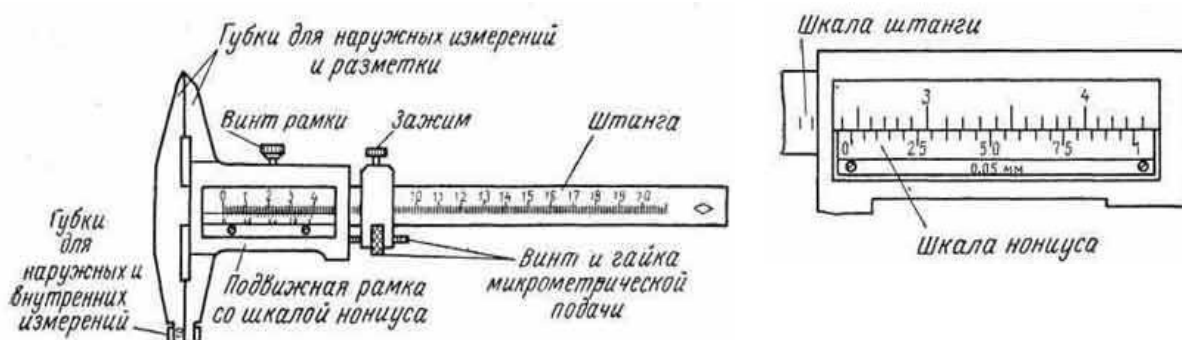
Конструкция штангенциркуля типа ШЦ-II
